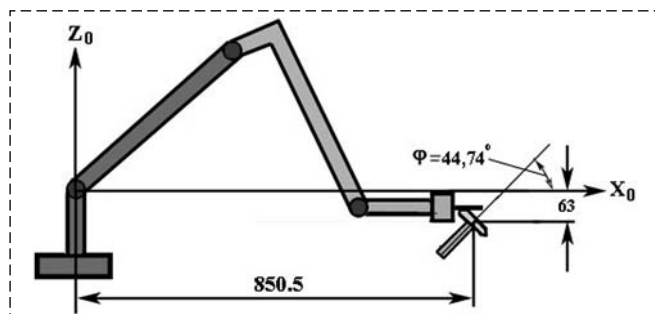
Компонка робота с лопаткой и инструмента с его приводом
